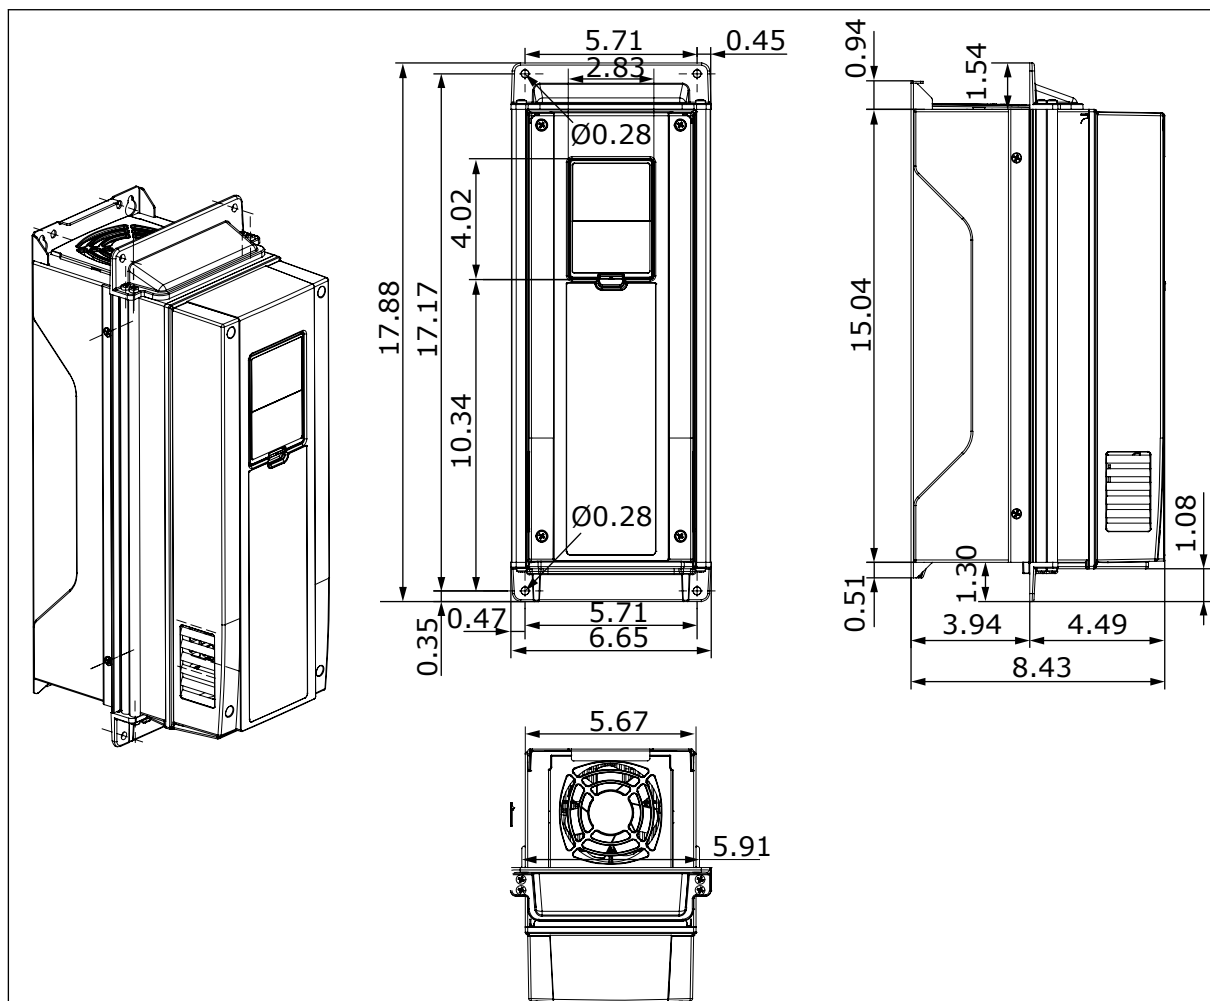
Dimensioni dell'inverter, montaggio a flangia, MR5 [pollici]
